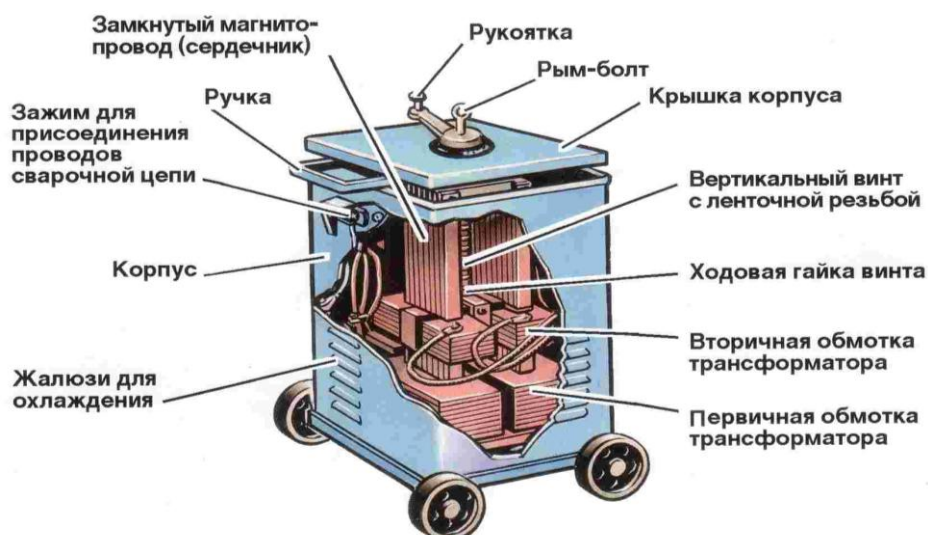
Внешний вид сварочного трансформатора
